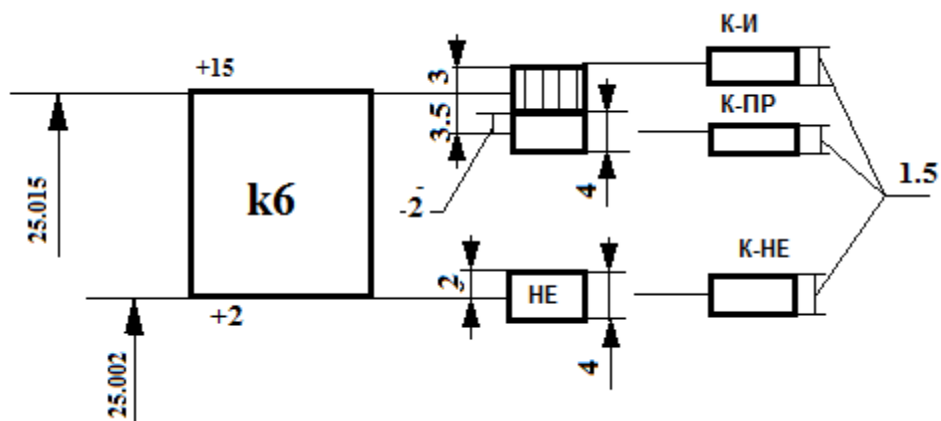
Схема расположения полей допусков калибров для вала  $\varnothing 25k6 \begin{matrix} +0,015 \\ +0,002 \end{matrix}$
